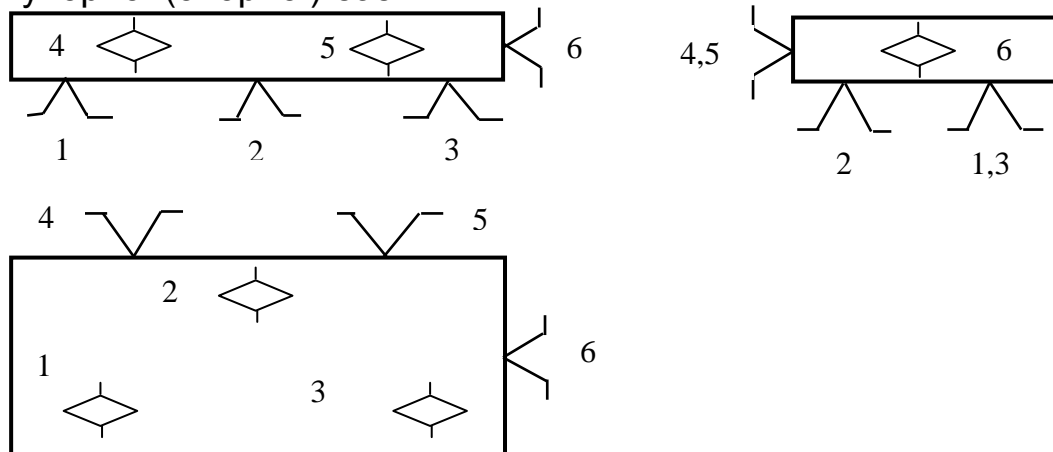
Схема базування призматичної заготовки по плоским поверхням
